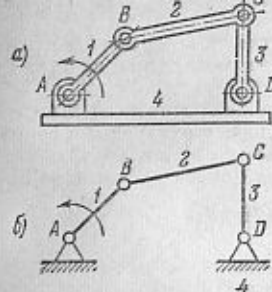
Плоский шарнирный четырехзвенный механизм: а) полуконструктивная схема, б) кинематическая схема.
